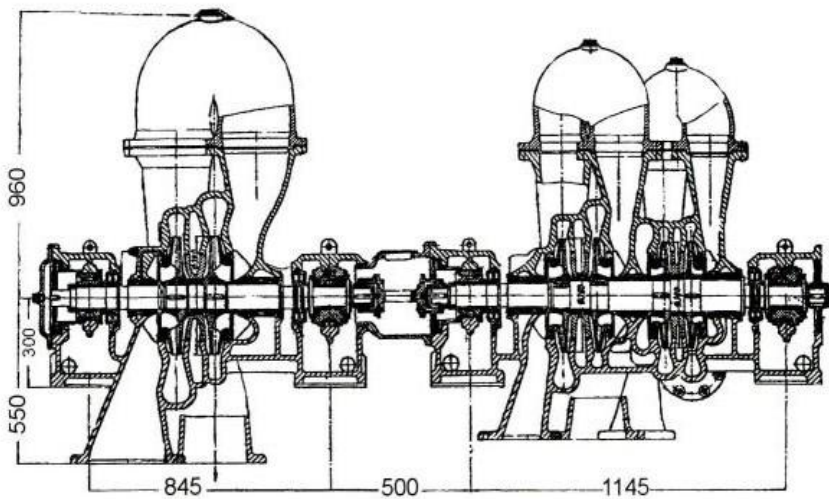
Двоборпусний компресор типу ТК-8
